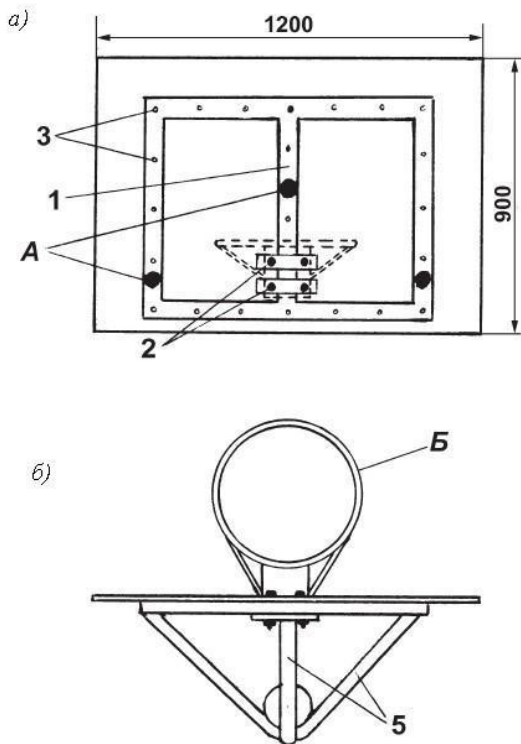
Вариант конструкции стойки для раздельного монтажа:
